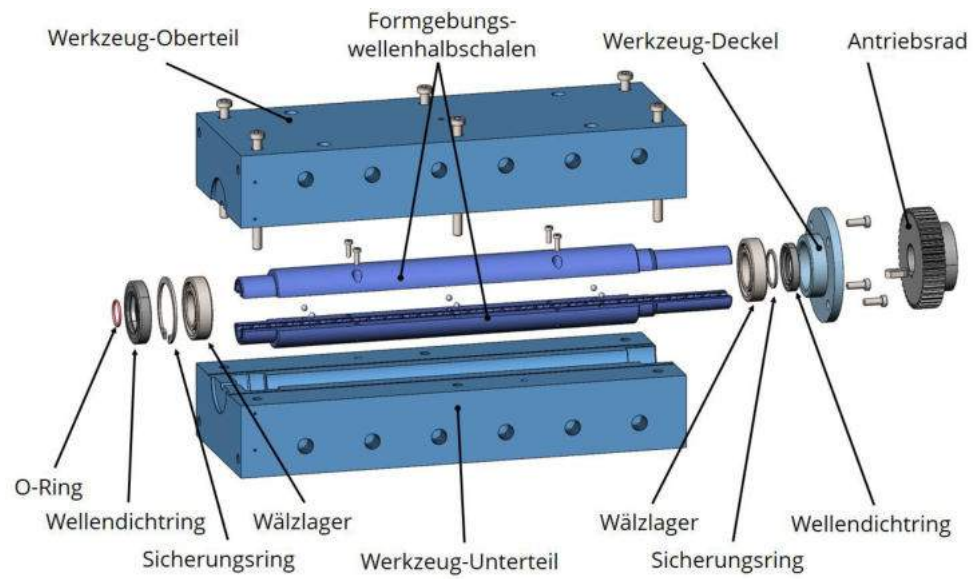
Finales Formgebungswerkzeugdesign
